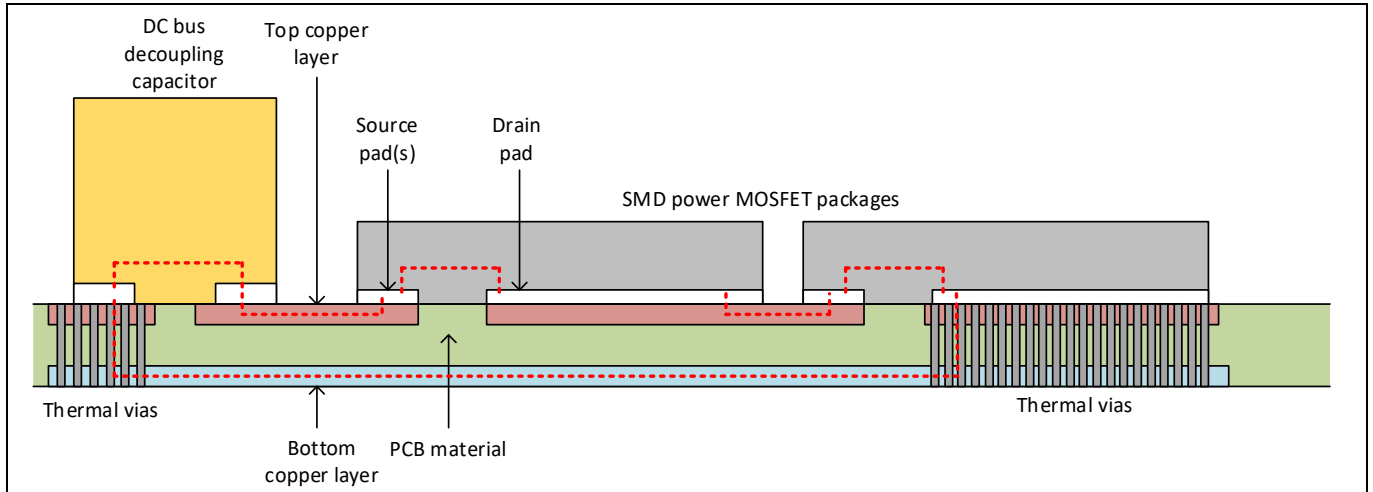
SMD MOSFET 封装的 PCB 布局优化示例
